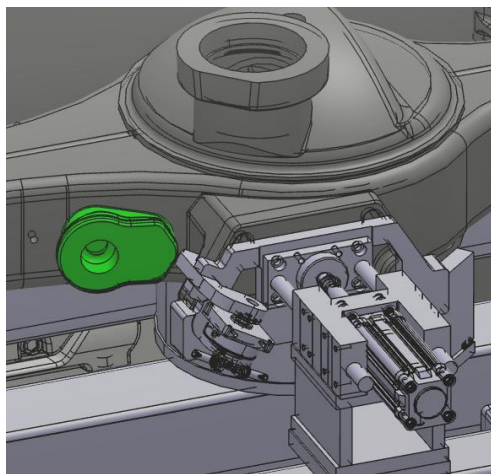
Jig* de soldadura para montagem manual de peças
